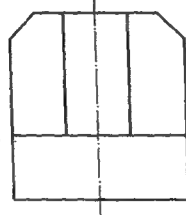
Dibujar el perfil del objeto representado mediante alzado y planta.
